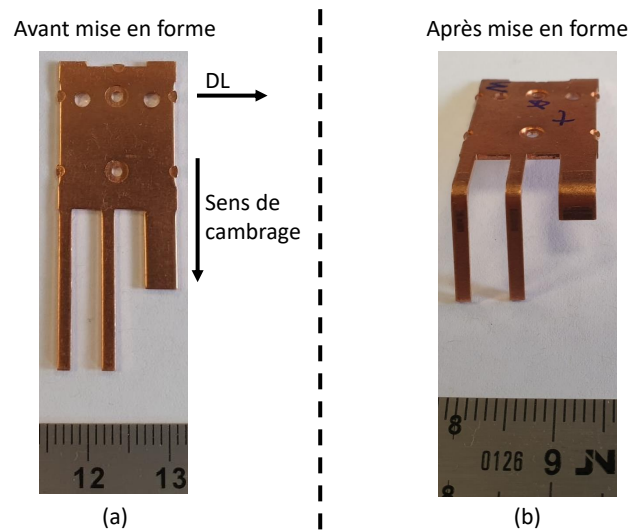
Éprouvette de la géométrie avec 3 contacts avant (a) et après (b) mise en forme
